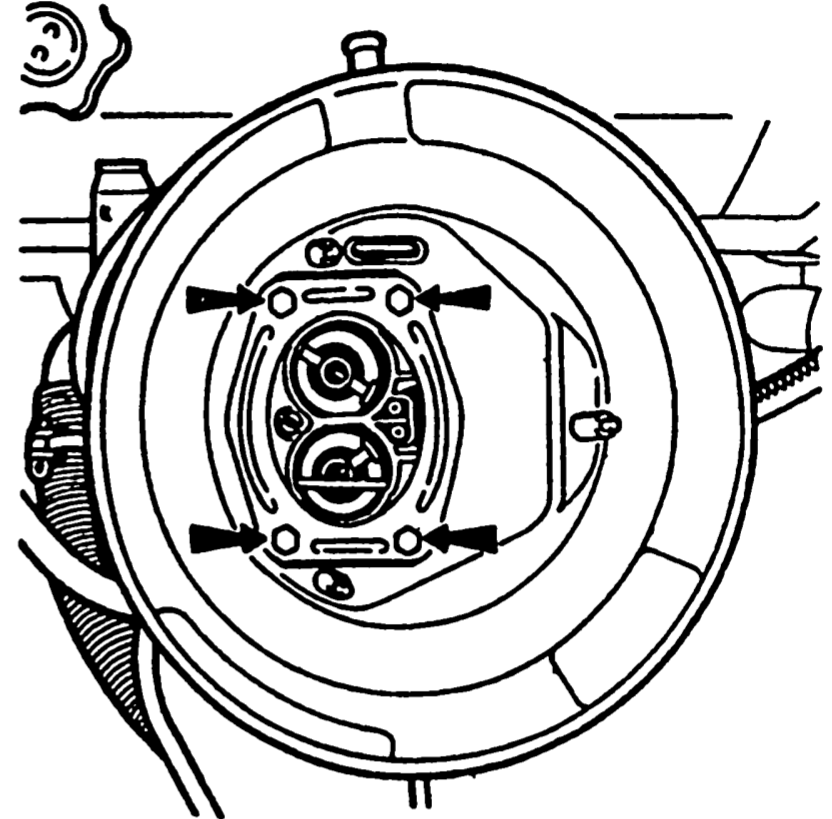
Снятие воздушного фильтра. Стрелками указаны гайки крепления корпуса фильтра к карбюратору
